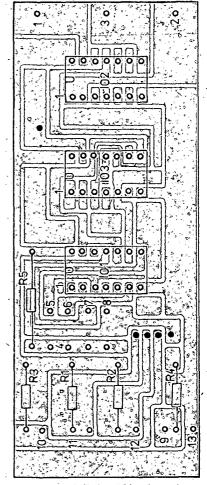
Obrazec plošných spojů desky čítačů a dekodérů (strana součástek) T119
